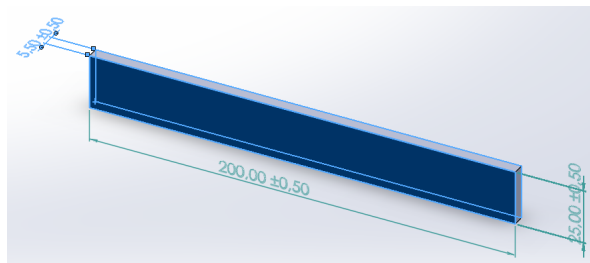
Taille des éprouvettes Résine Seule
